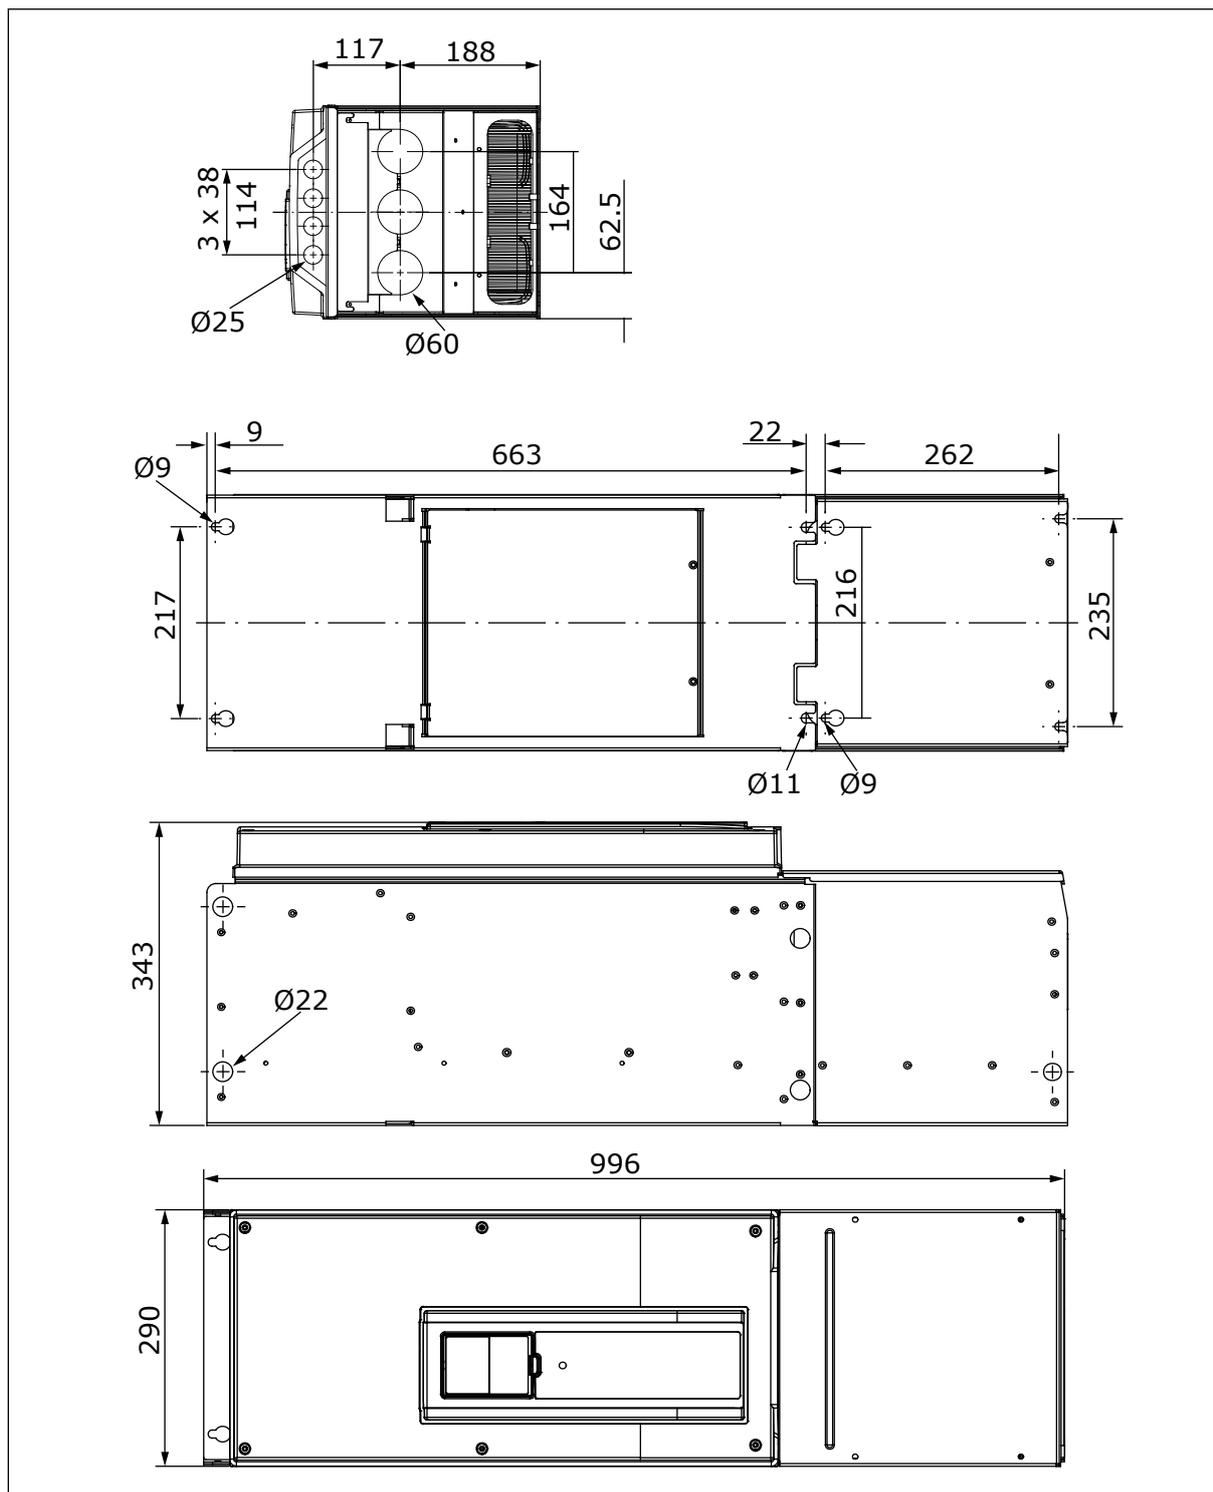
Dimensões do conversor de frequência, MR8, IP21 e IP54 [mm]
